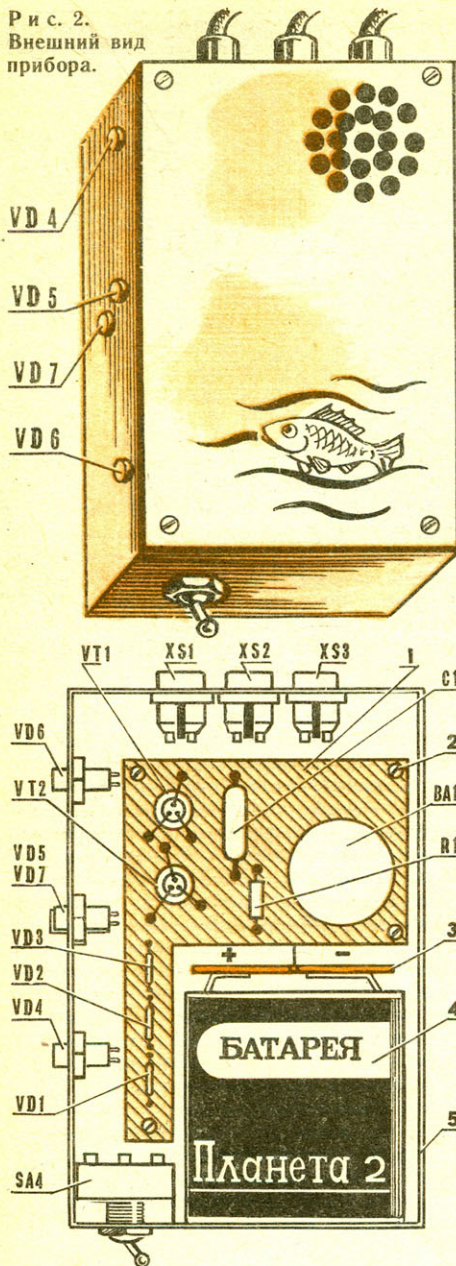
Внутренняя компоновка: 1 — плата, 2 — винт крепления, 3 — контактная планка, 4 — батарея питания, 5 — корпус.
